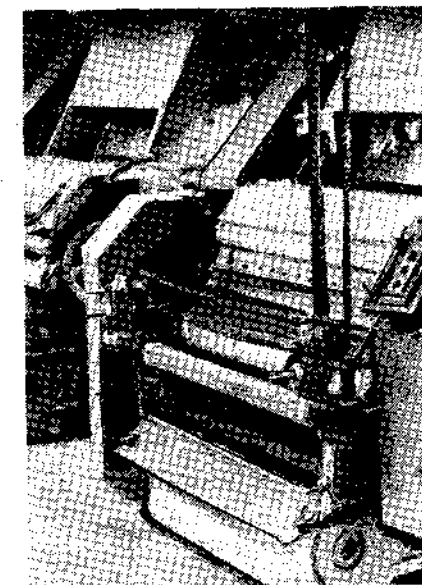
Общий вид валичного джина с зубчато-винтовым прижимным устройством
